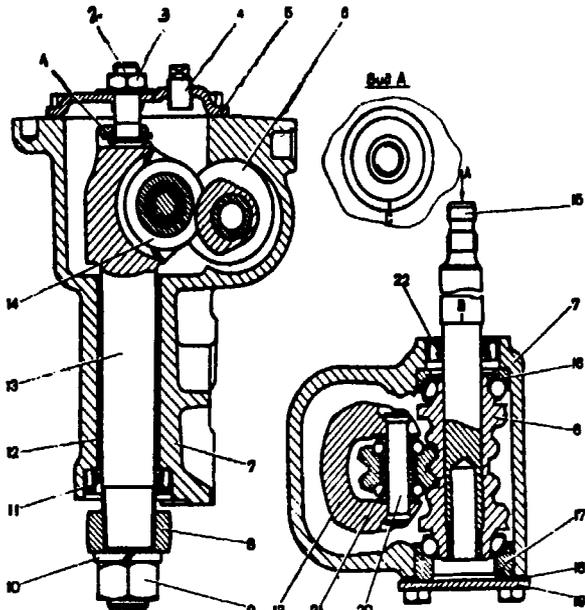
Разрез картера рулевого механизма: 1 - пластина регулировочного винта вала сошки; 2 - регулировочный винт вала сошки; 3 - гайка регулировочного винта; 4 - пробка маслониловного отверстия; 5 - крышка картера рулевого механизма; 6 - червяк; 7 - картер рулевого механизма; 8 - сошка; 9 - гайка крепления сошки к валу; 10 - шайба пружинная; 11 - сальник вала сошки; 12 - втулка вала сошки; 13 - вал сошки; 14 - ролик вала сошки; 15 - вал червяка; 16 - верхний шарикоподшипник; 17 - нижний шарикоподшипник; 18 - регулировочные прокладки; 19 - нижняя крышка подшипника червяка; 20 - ось ролика; 21 - шариковый подшипник ролика; 22 - сальник вала червяка; В, С - метки
